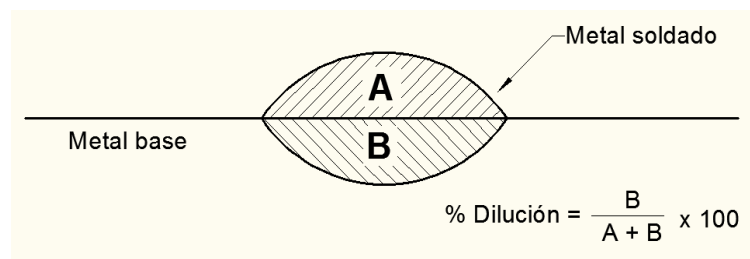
23. Esquema de dilución de un cordón de soldadura [1].
